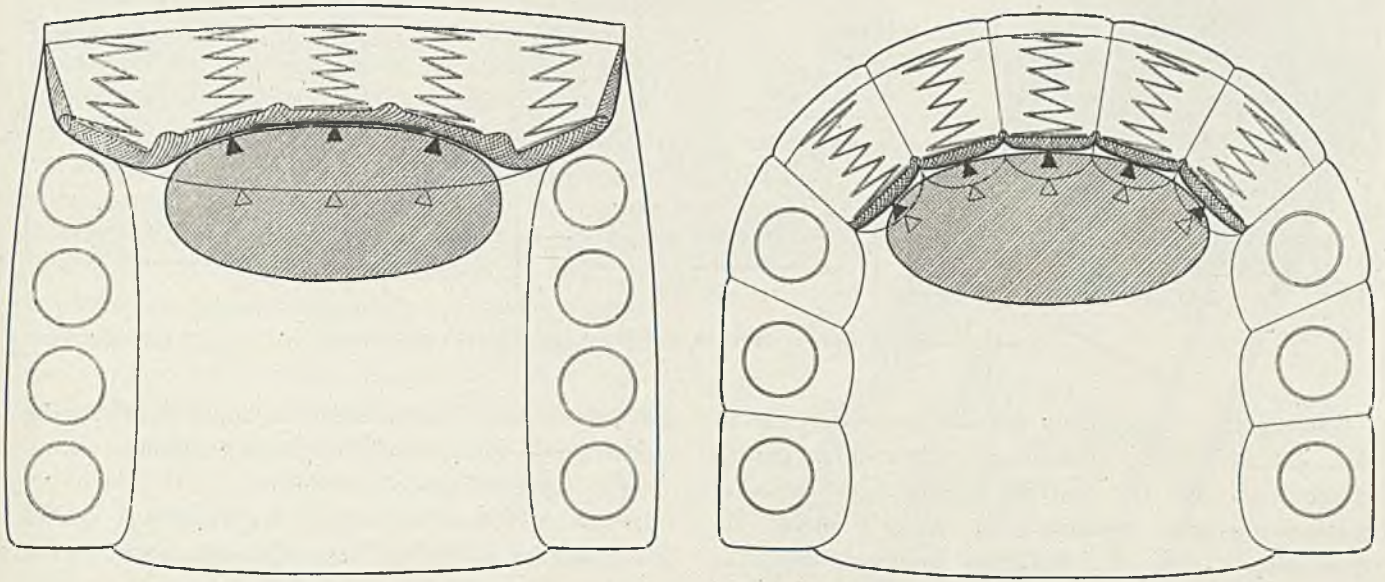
/355. Grundrißschema zweier Sessel auf eckigem und halbrundem Grundriß mit Schnitten durch deren Rücklehnen
